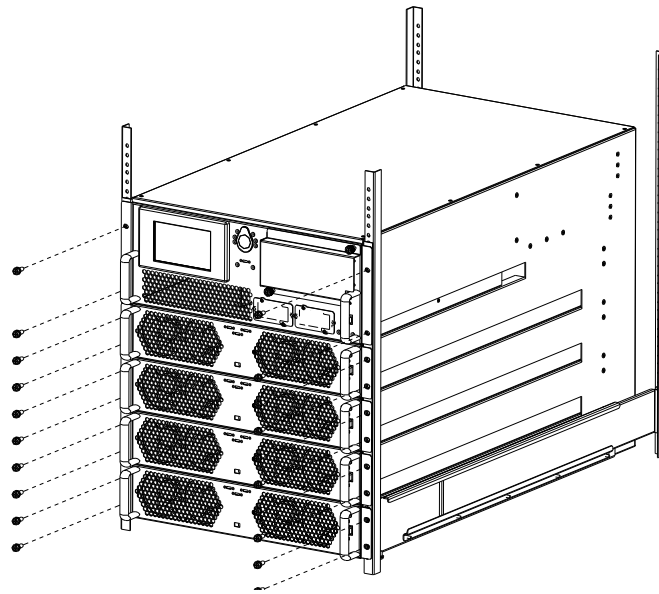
Установка корпуса ИБП в шкаф. Крепление плавающими гайками
